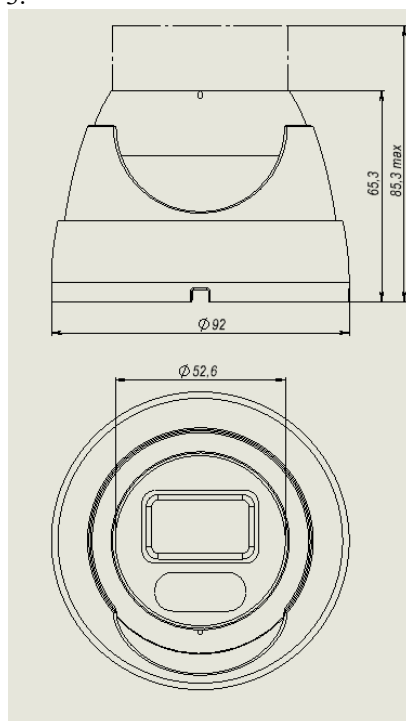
Внешний вид видеокамеры EVM2-IPx корпус KP23
